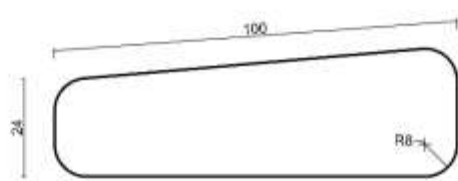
Desenho técnico peça "D" (Fonte: o autor)
